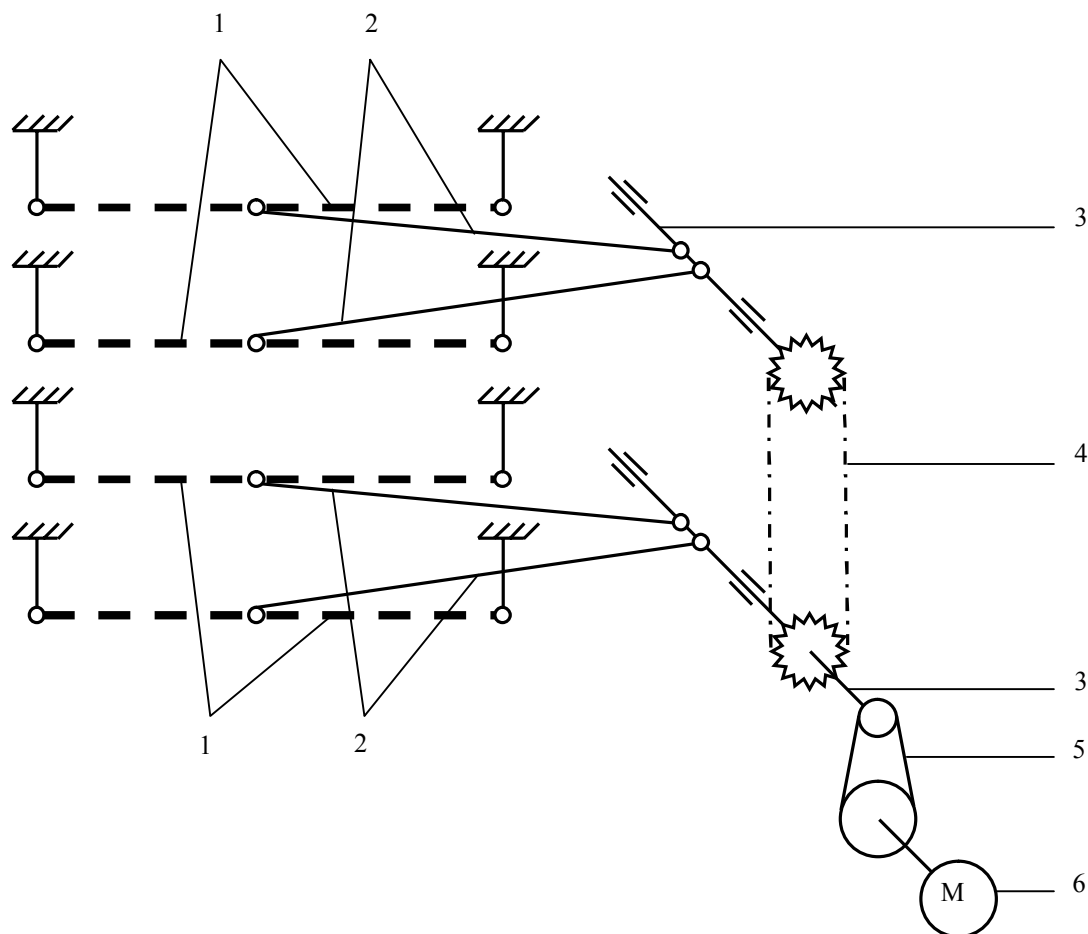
Кинематическая схема ОЗС-50: 1 – решетные станы; 2 – ползуны; 3 – эксцентриковые валы; 4 – цепная передача; 5 – клиноременная передача; 6 – электродвигатель
